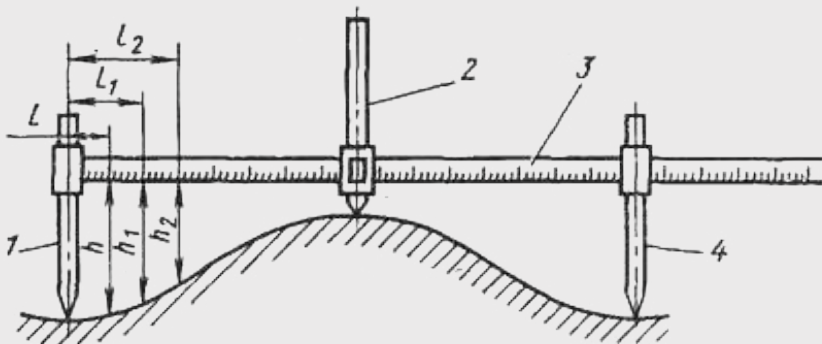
Вимірювання фасонної поверхні у прямокутних координатах: 1, 4 — контрольні щупи; 2 — вимірювальний щуп; 3 — лінійка; l_1 , l_2 — задані координати; h , h_1 , h_2 — координати точки вимірюваної поверхні
